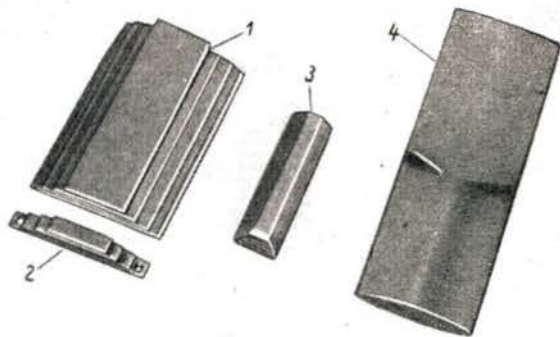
Herstellung von Federpaketen, Sandkästen und Ausgleichhebeln; 1 Zusammengelötete Blechstreifen, 2 abgesägtes Federpaket, 3 zugefeilter Profilstab für Sandkästen, 4 zugefeilter Profilstab für Ausgleichhebel
